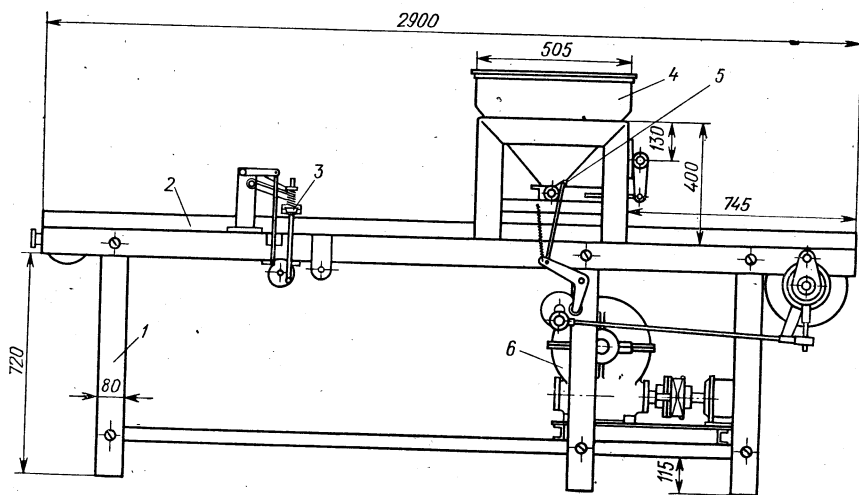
Машина для отливки ликерных корпусов в крахмал:
